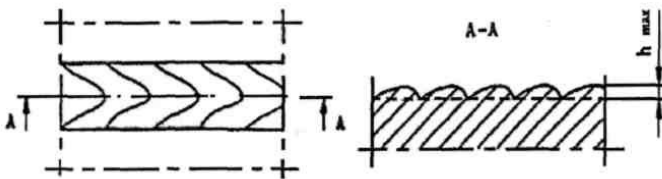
19. Чешуйчатость сварного шва
